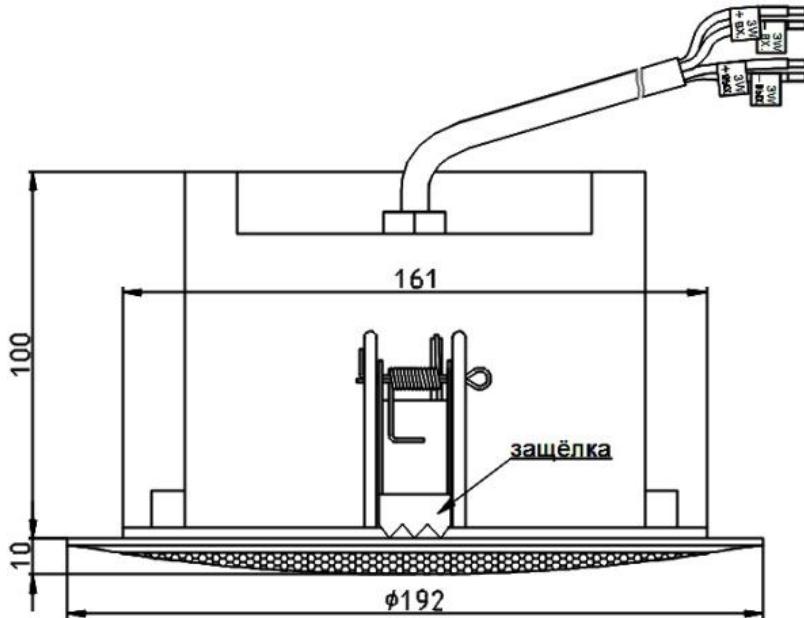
Внешний вид (вид сбоку) и габаритные размеры оповещателя
